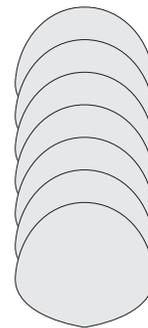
Недостаточное перекрытие сварочных ванн
